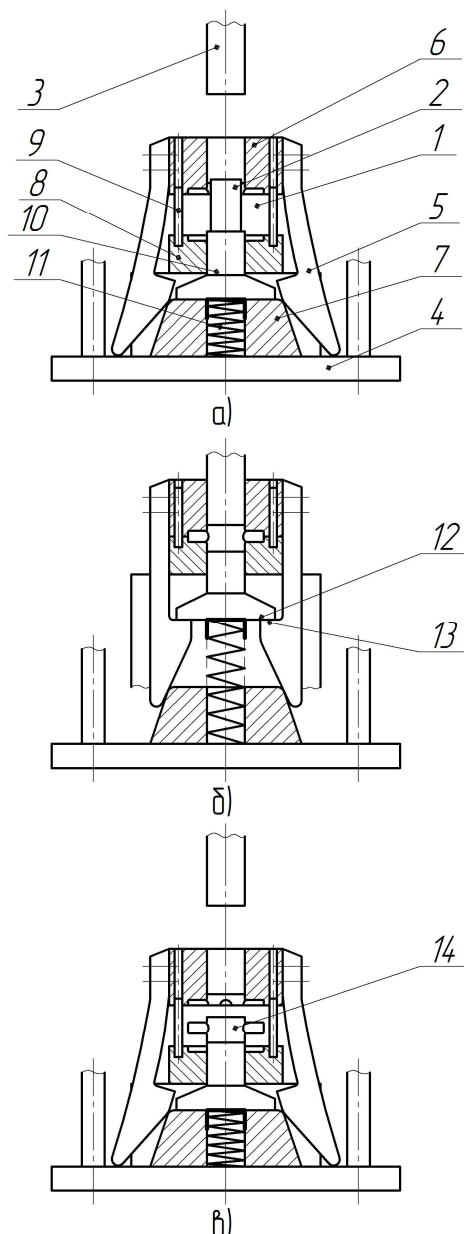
Принципиальная схема записания матриц с поперечной плоскостью разъема: а) – начальный момент штамповки с загруженной заготовкой; б) – непосредственная штамповка; в) – окончательный момент штамповки с готовой поковкой
